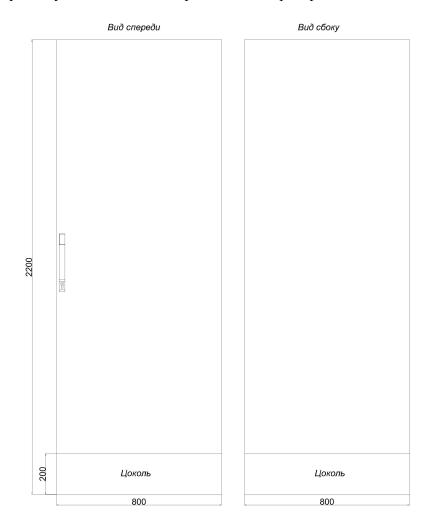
Внешний вид и габаритные размеры концентратора с одностворчатыми дверями
